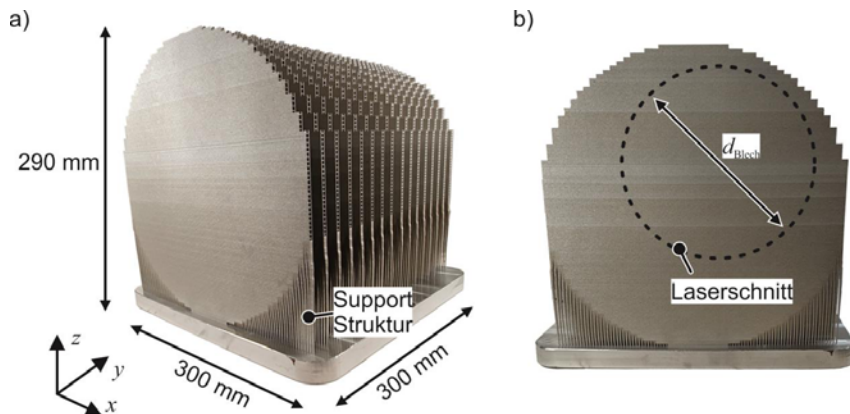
a) Additiv gefertigte Blechhalbzeuge auf der Bauplattform, b) Frontansicht vor dem Post-Processing und dem Laserschnitt
